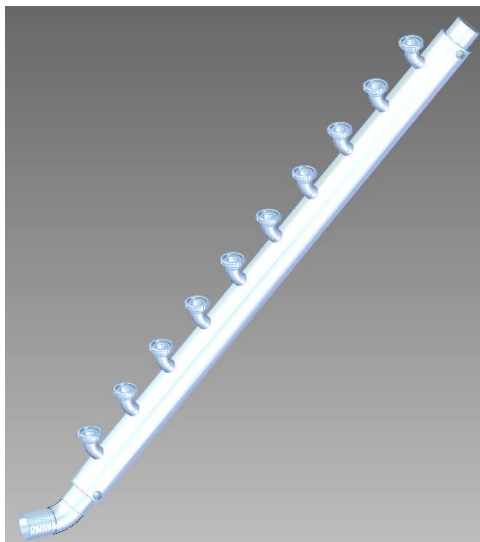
Particolare collettore su struttura stoccaggio creme (Solid Edge)
